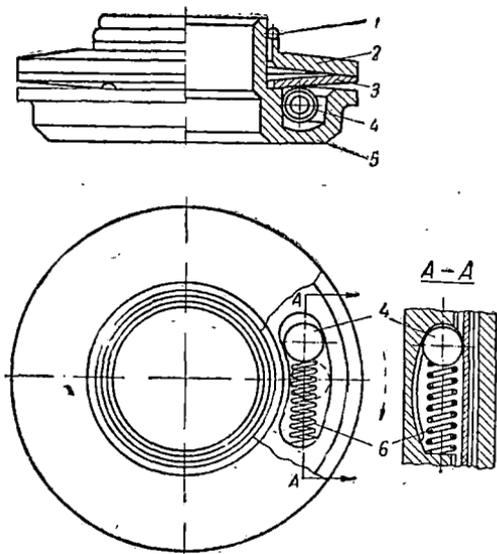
Устройство для поворота выпускного клапана (ЗИЛ-111):
